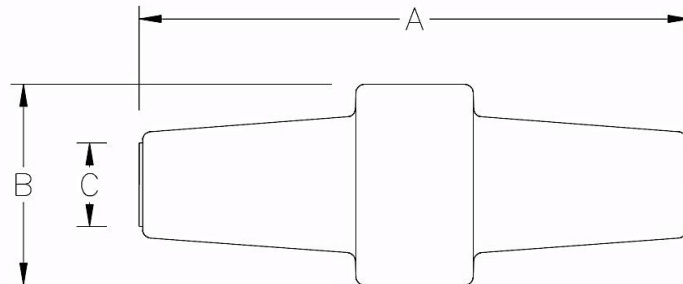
Dimensiones de inserto tipo "BUSHING" 600 A, [12].
